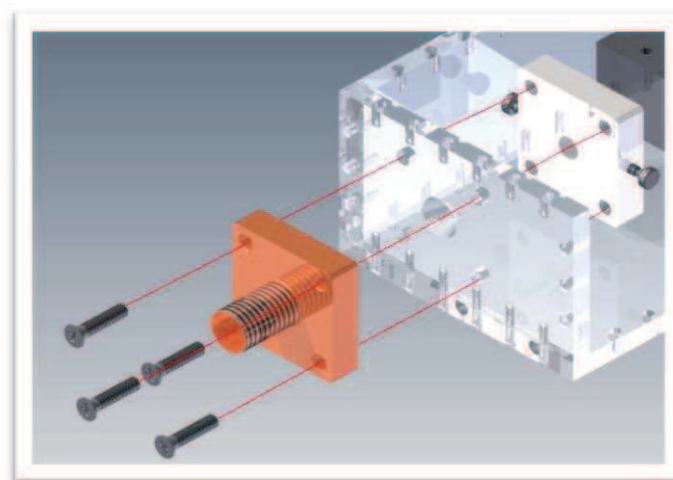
Ensamble asiento-carcasa- placa roscada
